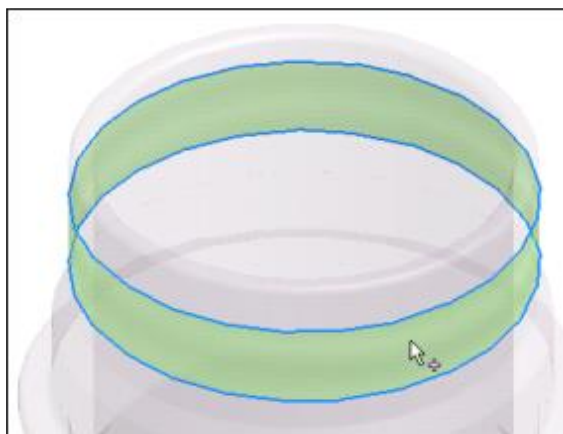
Розділяємо поверхню деталі до якої застосовуватиметься інструмент «Різьба»
